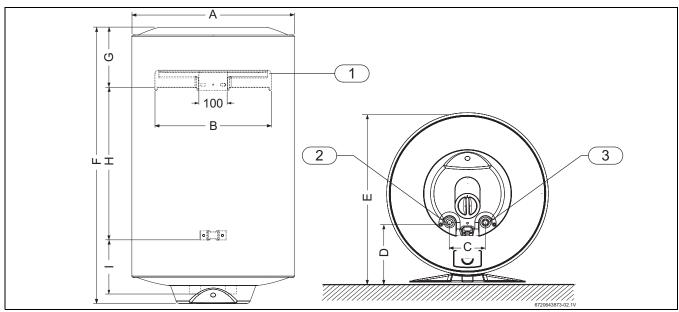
Dimensões em mm (ES030/050/075/100-1...)
